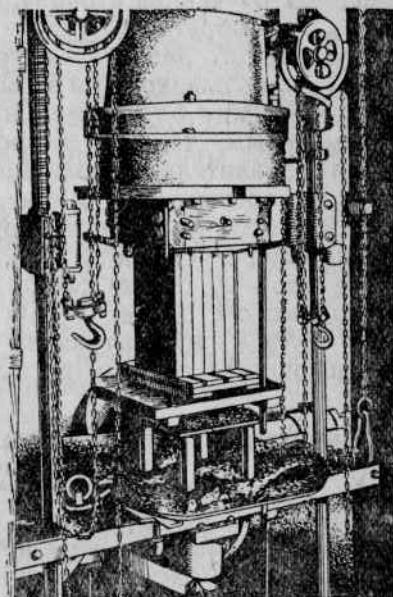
Формовка блоков на вертикальном трубном прессе.
